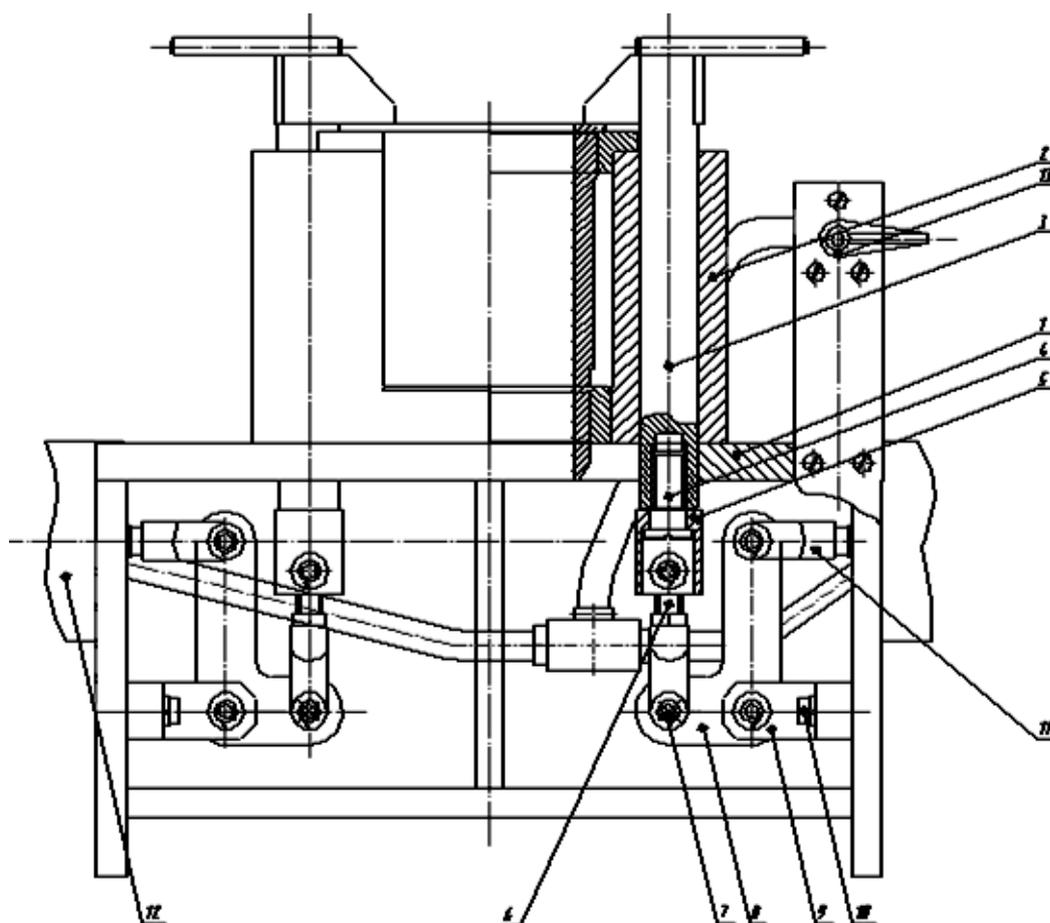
Приспособление для закрепления гильзы цилиндров
